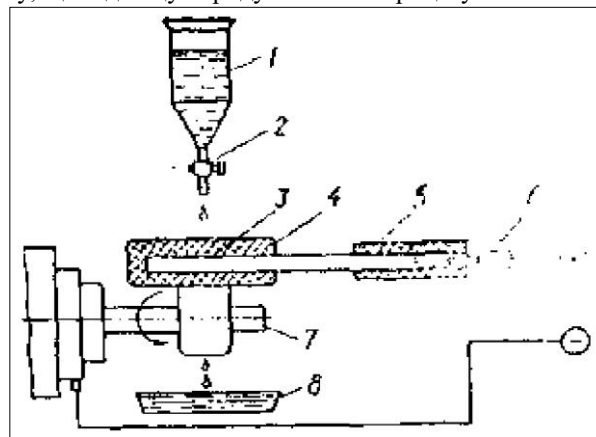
Схема установки для електролітичного натирання металу:
